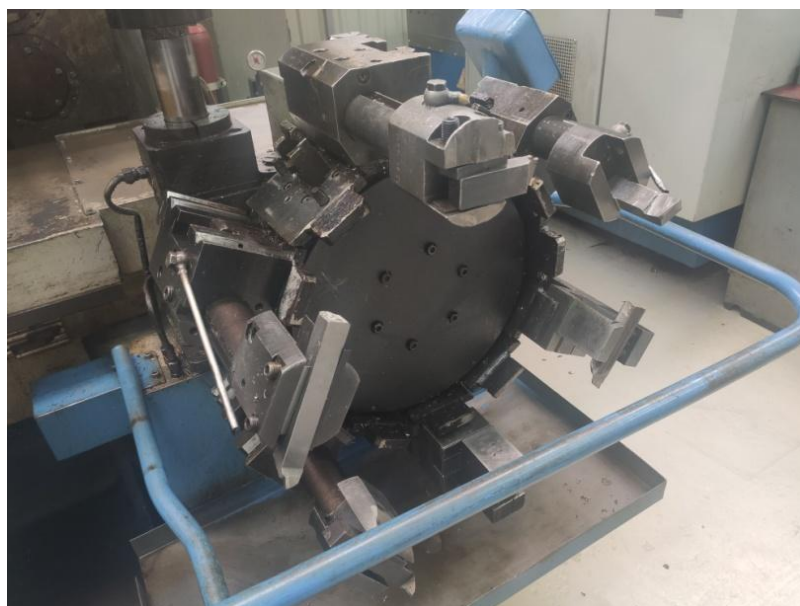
Зовнішній вигляд інструментальних блоків
